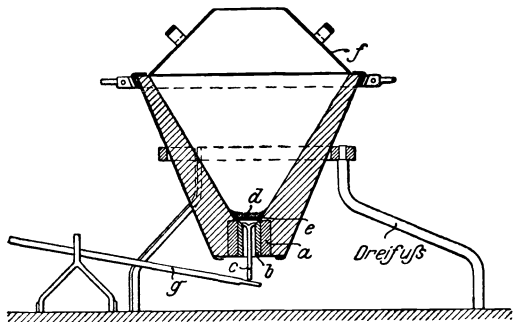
Spitztiegel für Thermitschweißung.
